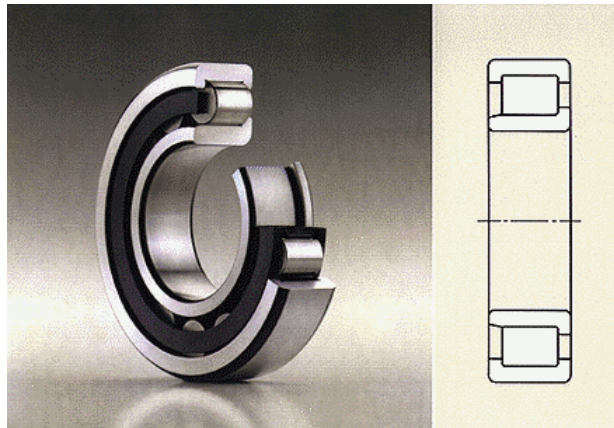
Rodamiento de rodillos cilíndricos de una sola hilera
